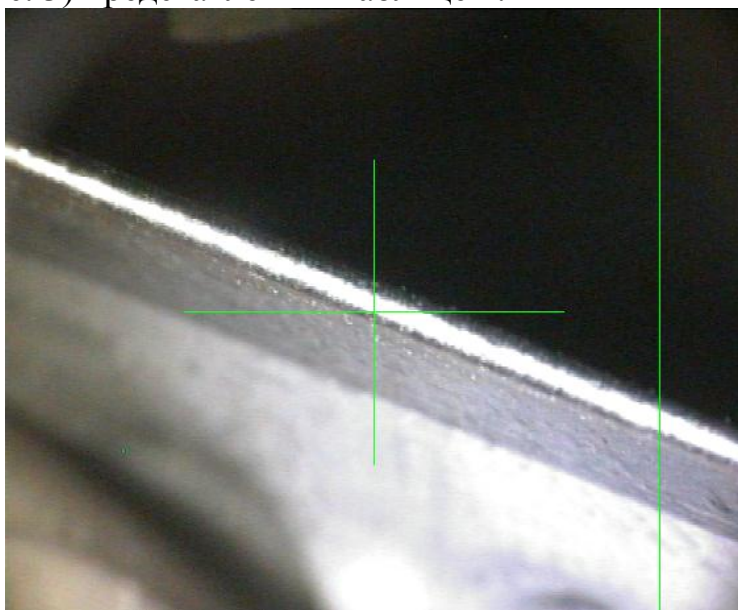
Сварной шов двух пластин одинаковой толщины
